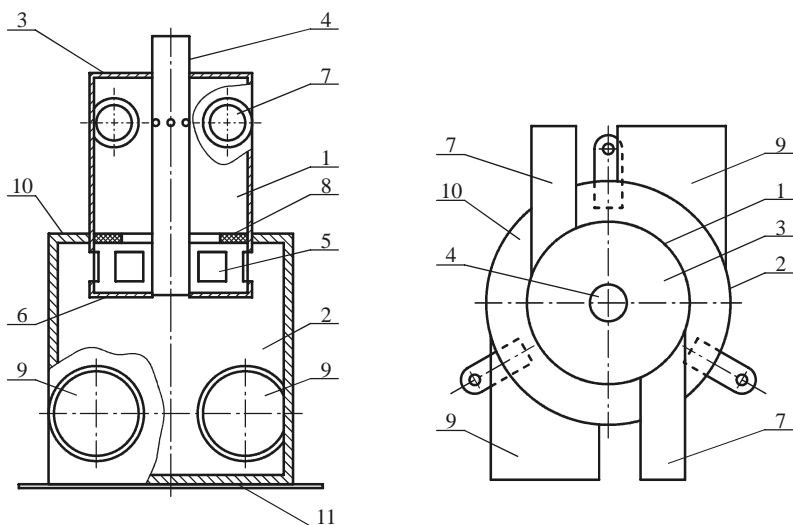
Конструктивная схема центробежно-вихревого деаэратора ДЦВ-670: 1 – корпус; 2 – центробежный сепаратор; 3 и 6 – соответственно верхняя и нижняя торцевые крышки корпуса; 4 – трубопровод отвода пара; 5 – окна для отвода воды из корпуса; 7 и 9 – соответственно подводящие и отводящие тангенциальные патрубки; 8 – кольцевая перегородка (шайба); 10 и 11 – соответственно верхняя и нижняя торцевые крышки центробежного сепаратора
